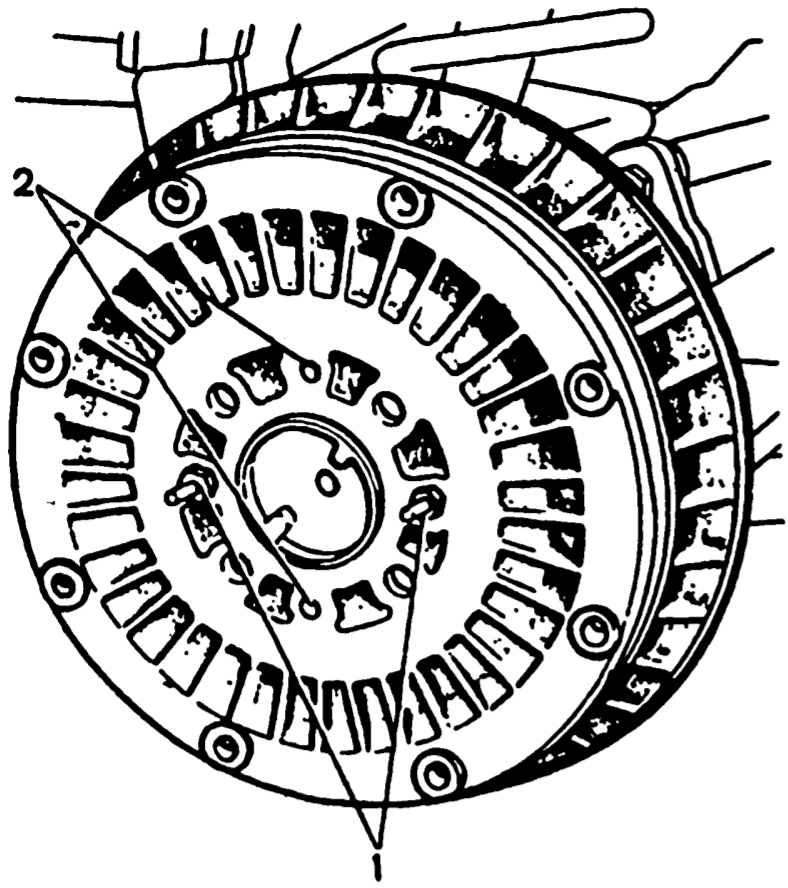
Тормозной барабан заднего колеса: 1 - болты крепления барабана к полуоси; 2 - резьбовые отверстия для установки болтов 1 при снятии барабана
